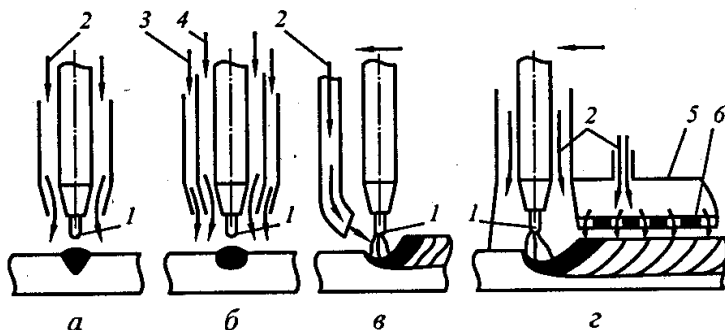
Схемы подачи защитных газов в зону сварки:
